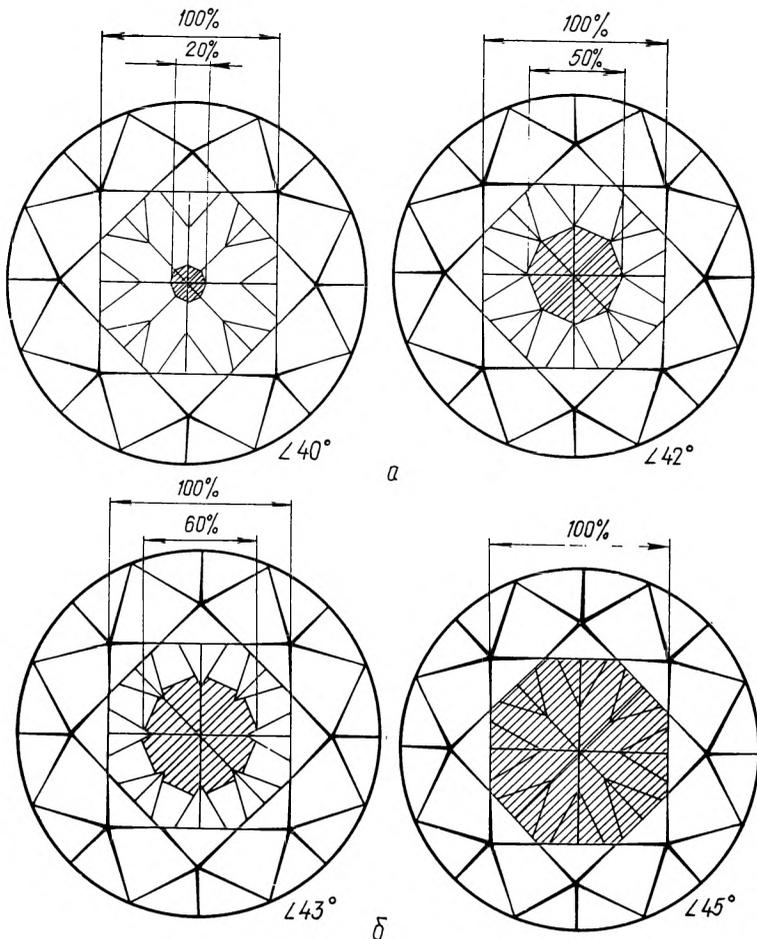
Визуальное определение угла наклона по отражению площадки от грани низа:
